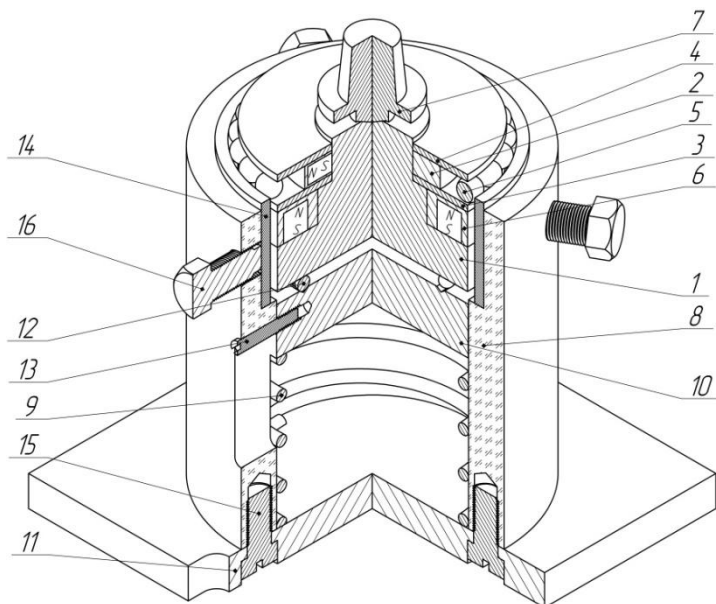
Конструкция устройства для отделочно-упрочняющей обработки:
